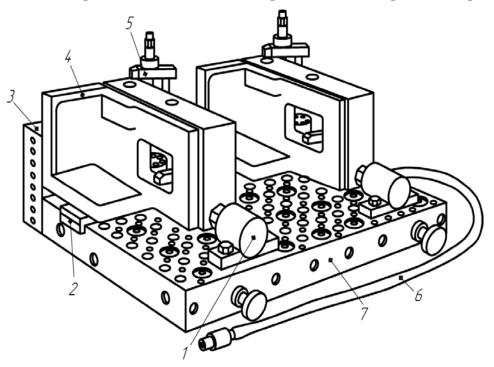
Двухместное гидравлическое приспособление для установки корпусной детали: 1 — горизонтальный гидроцилиндр; 2 — опорная планка; 3 — угольник; 4 — заготовка; 5 — прихват; 6 — шланг; 7 — гидрофицированная плита
